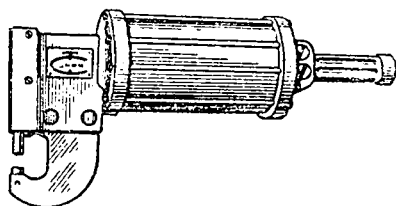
Ручной переносный пневматический пресс ПРП5-2 для одиночной клепки
